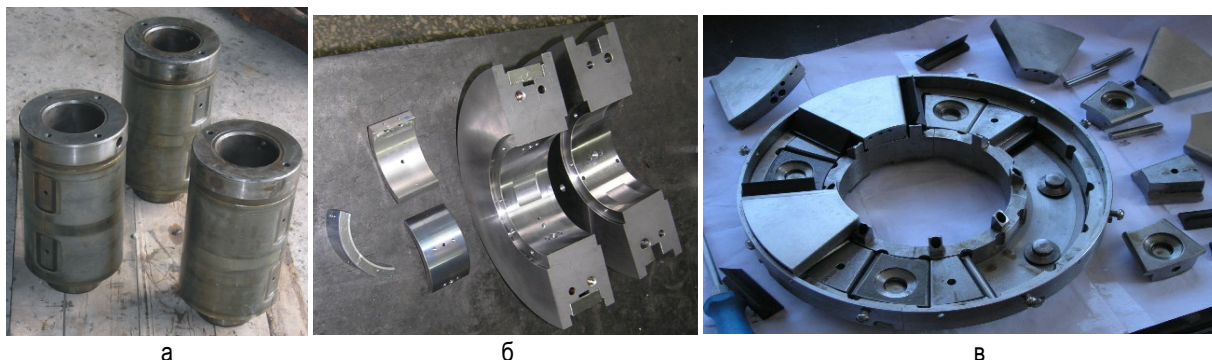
Конструктивні елементи ПК з бабітових покриттям: а - зовнішня поверхня опорних пальців зубчастих коліс, б - внутрішня поверхня вкладишів опорних ПК, в - плоска поверхня напольгивої ПК.
